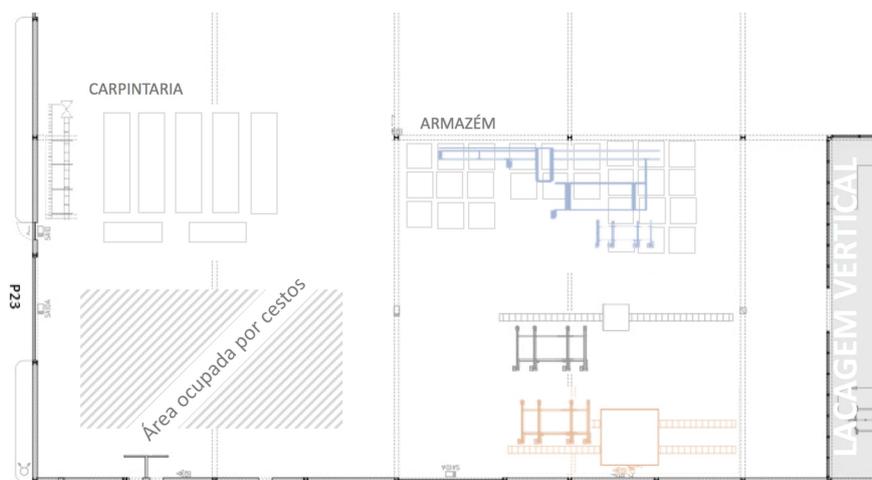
Planta inicial e futuras alterações consequentes das deslocações de máquinas de corte
